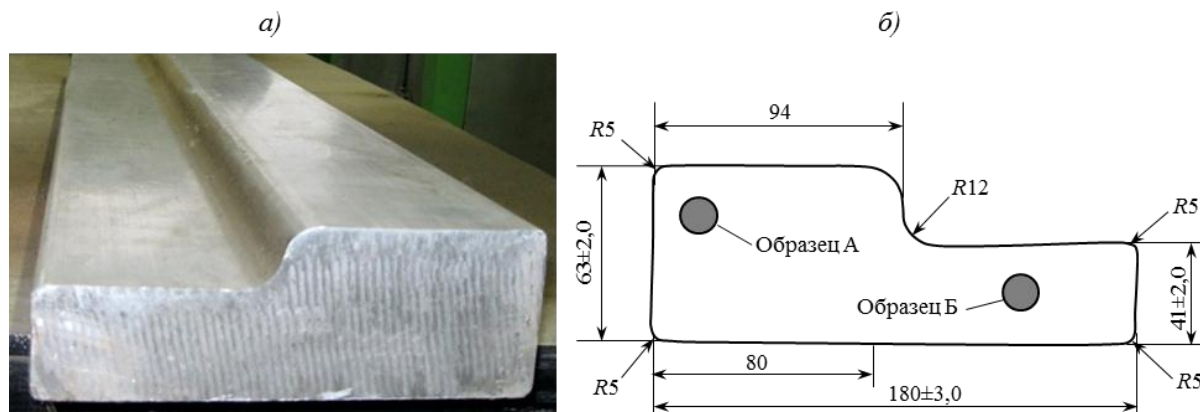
Внешний вид прессованного профиля шифра НП10 из сплава В-1341 (а) и схема его сечения (б)
